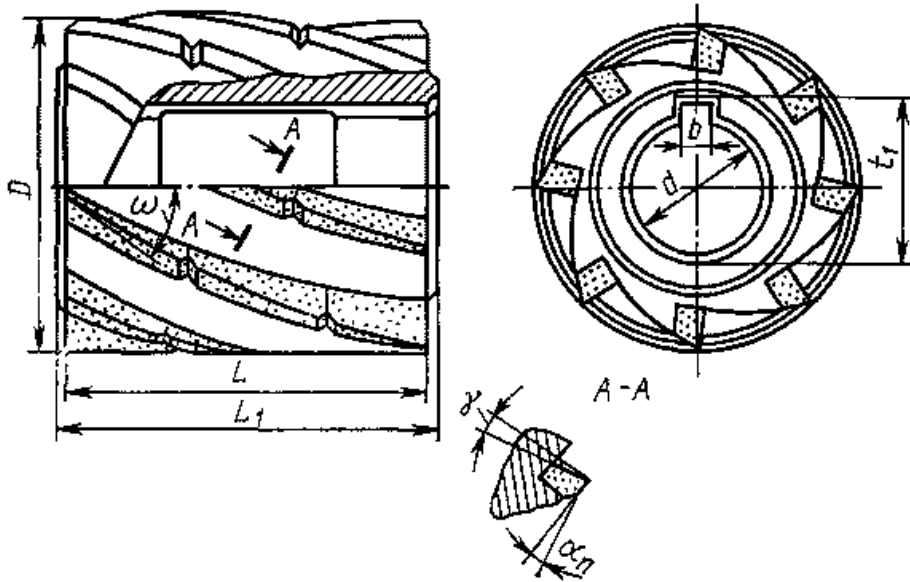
Циліндрова з гвинтовими зубами та з наплавками з твердого сплаву.
